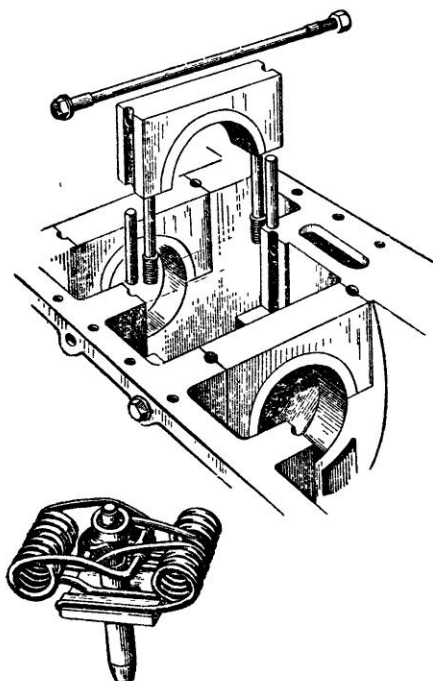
Крепление коренных подшипников и шпилечная пружина
